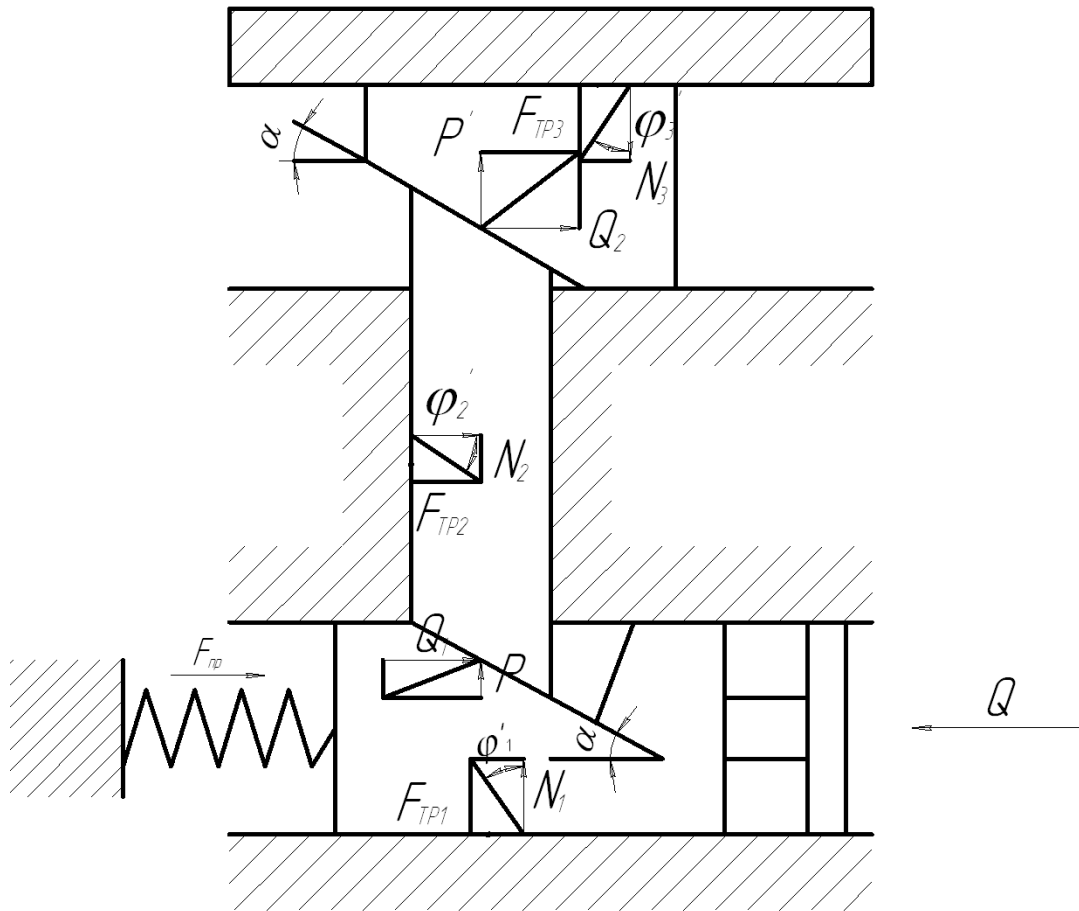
Схема для розрахунку сил затиску клино-плунжерного механізму.
